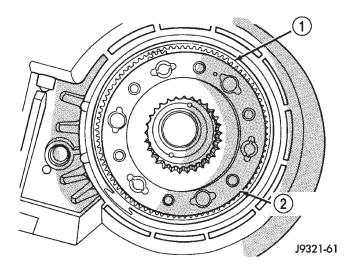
Instalación de los engranajes impulsor y de escala de baja
